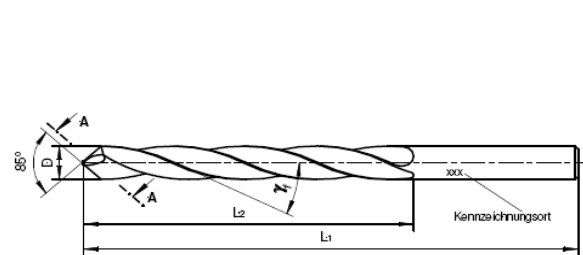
VHM-Werkzeug – Spiralbohrkopf
